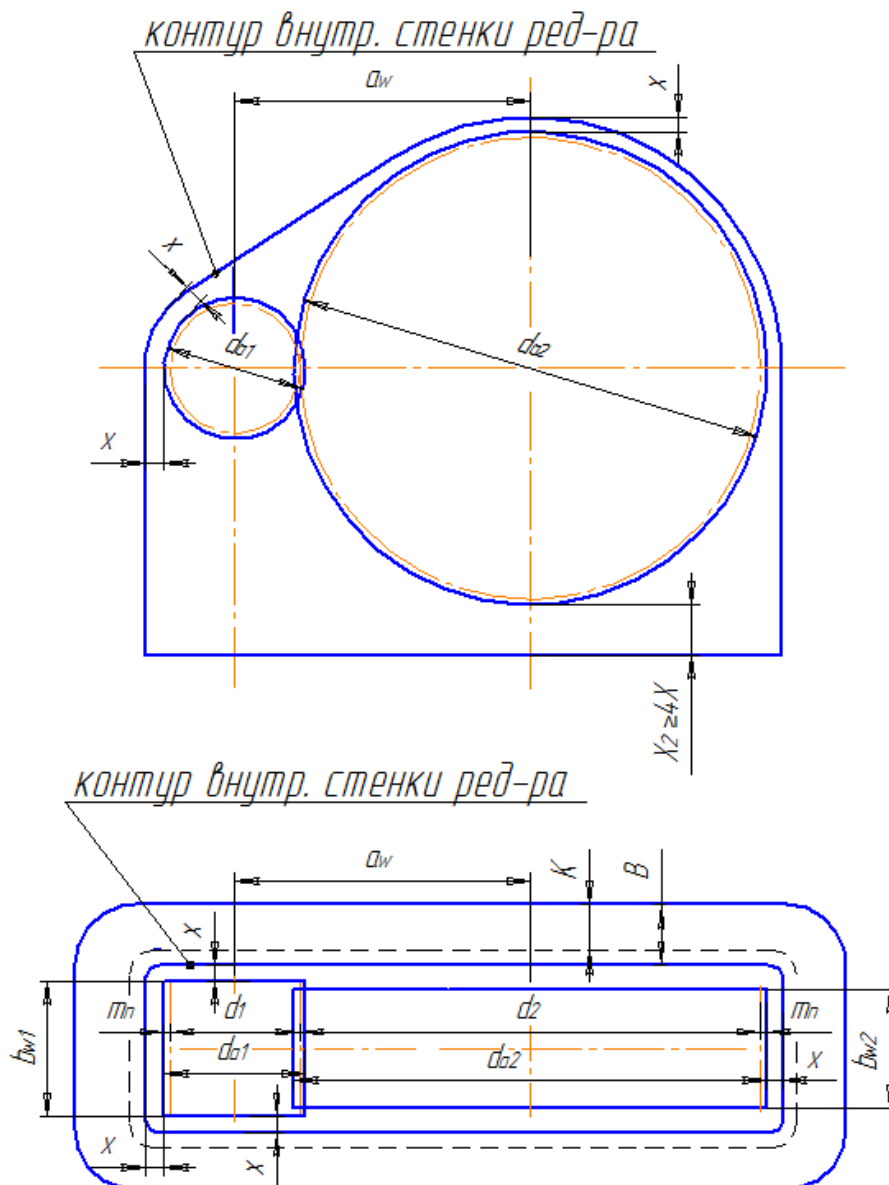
Первый этап эскизной компоновки одноступенчатого цилиндрического редуктора
